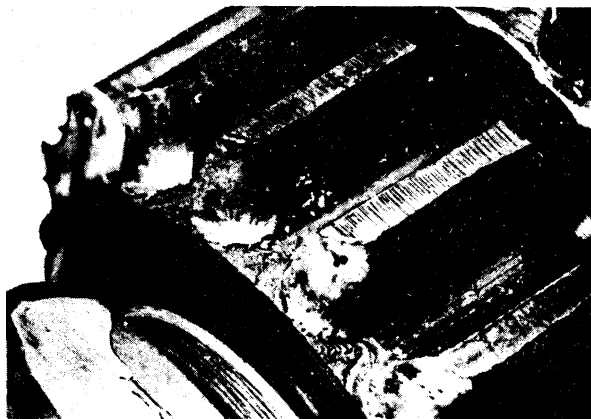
Усталостное разрушение торцевых поверхностей зубьев.
